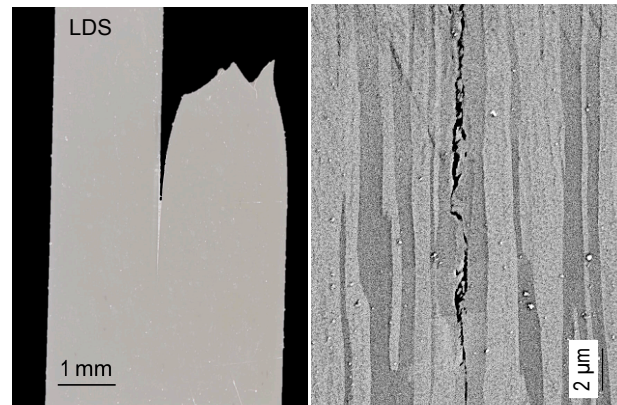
Perfil de rotura a tracción y frente de fisuración axial de los alambres prefisurados de acero dúplex LDS.
